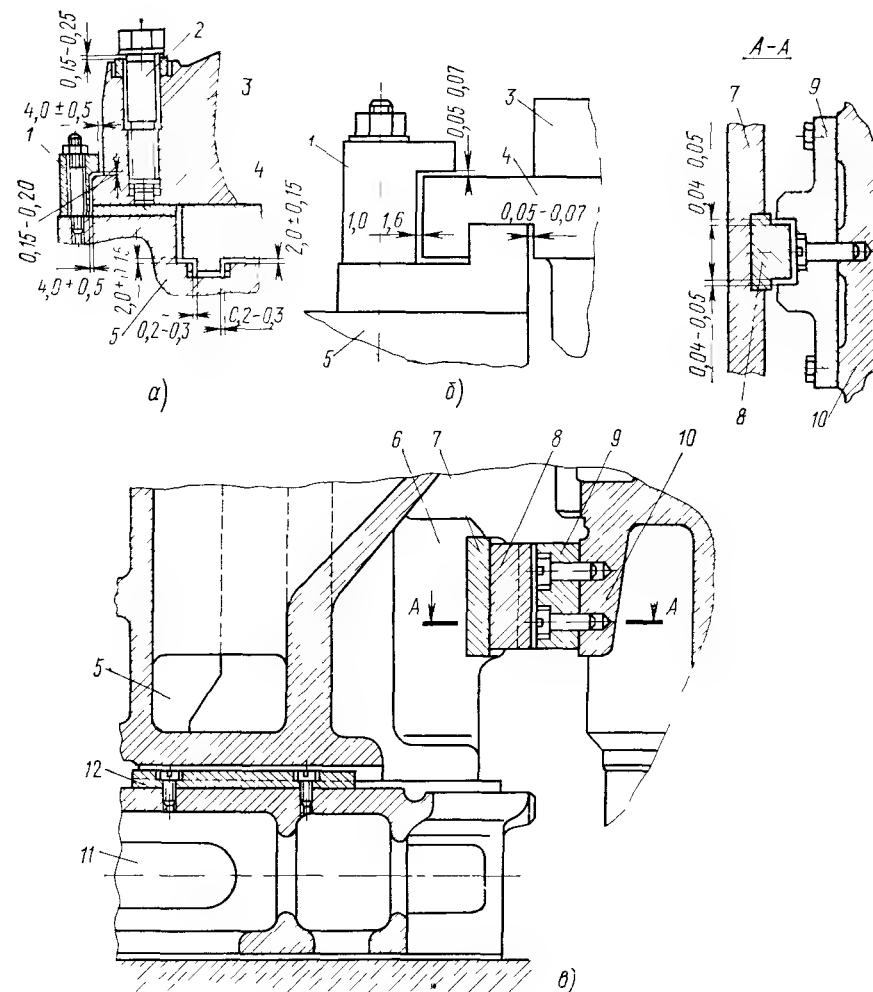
Опоры корпуса на стул подшипника, применяемые в турбинах ХТГЗ (а) и ЛМЗ, ТМЗ (б) и соединение корпуса турбины с корпусом подшипника (в)
